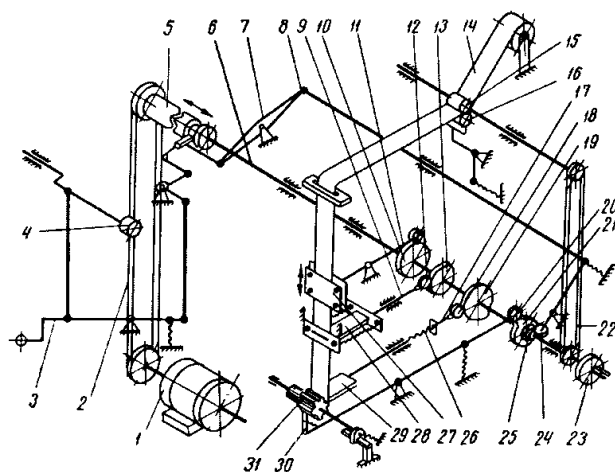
Кинематическая схема станка для изолировки пазов якоря.
